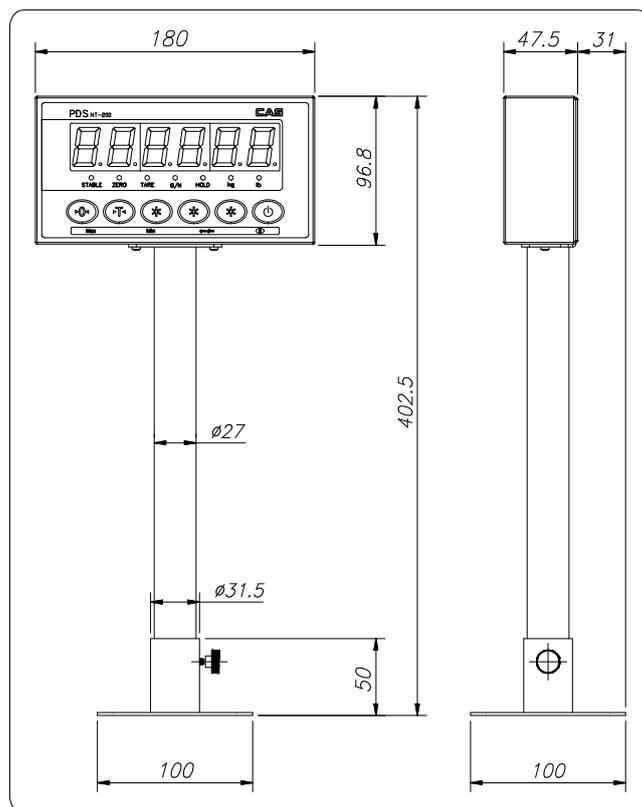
Габаритные размеры индикаторной головки в сборе со стойкой для исполнения «S».
